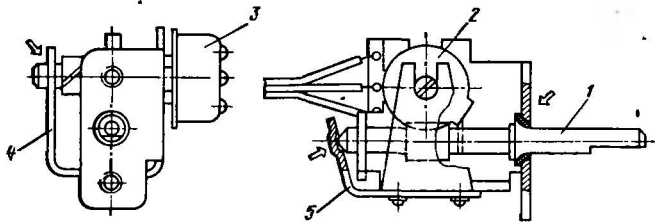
Механизма плавной настройки радиоприемника автомагнитолы «Былина РМ-317СА»: 1 — вал ручки настройки; 2 — зубчатое колесо; 3 — резистор типа СПЗ-4аМ; 4 — скоба; 5 — пружина (Стрелкой  $\Rightarrow$  показаны места смазки механизма настройки)
